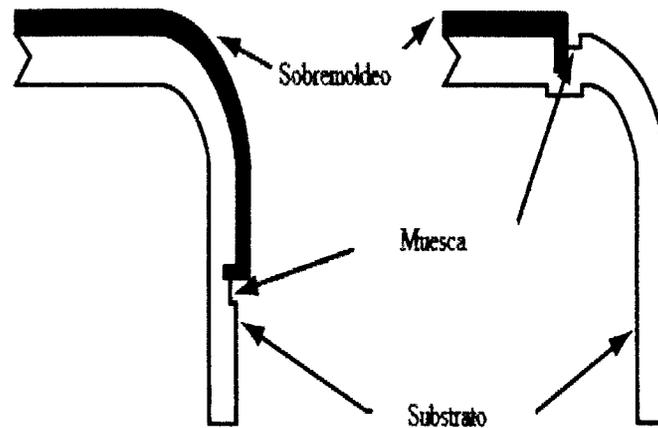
Técnica de sobre-moldeo por acoplamiento mecánico de partes.
